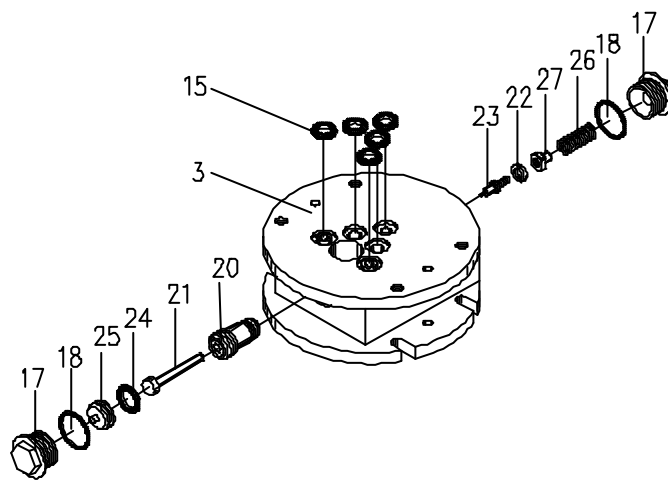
Piastra di montaggio per adattatore AEMD 4500 per robot
